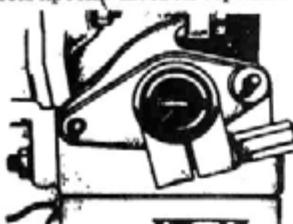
Положение паза на валике привода распределителя зажигания после установки привода на двигатель
